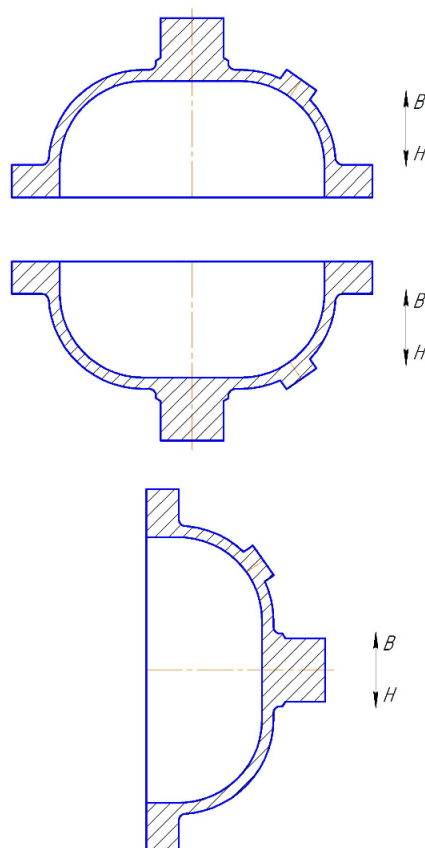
Варианты расположения отливки в форме в период заливки и затвердевания
